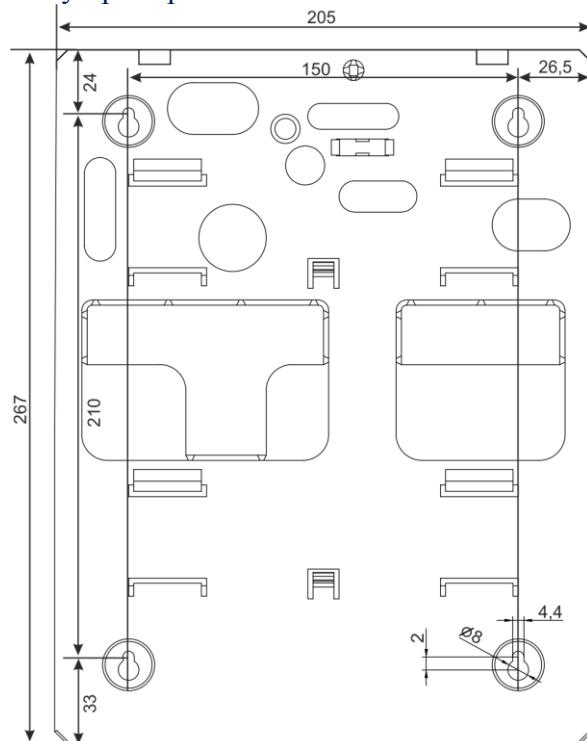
Установочный чертеж основания корпуса ППКО серии «А12»
